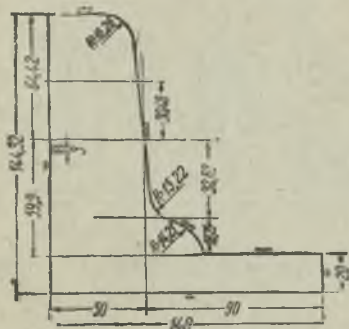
Шаблон для проверки внутреннего контура кокиля (допуски на размеры рабочих частей шаблона не должны превышать  $\pm 0,085$  мм)
